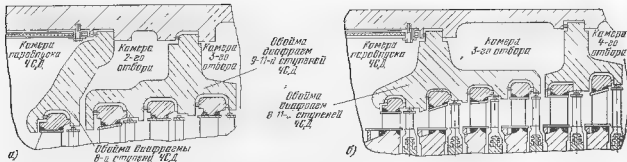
Конструкция ЧСД цилиндра высокого давления
